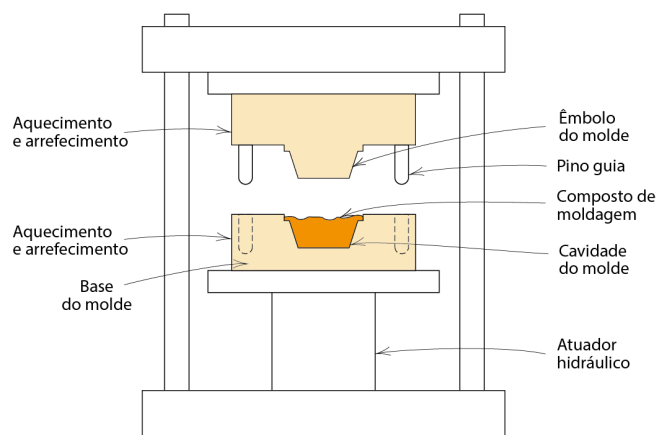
Representação esquemática de um aparelho de moldagem por compressão (adaptado de [21]).
